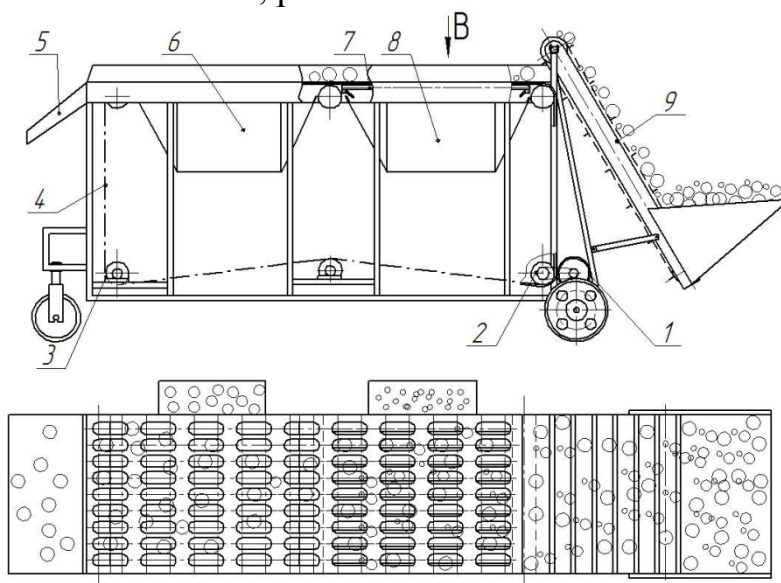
Схема запропонованої конструкції, з новим робочим органом транспортерного типу: 1 – приводний мотор-редуктор; 2 – ведучий барабан; 3 – підтримувальний барабан; 4 – транспортерна стрічка; 5 – лоток приймання великої фракції; 6 – лоток приймання середньої фракції; 7 – калібрувальне решето; 8 – лоток приймання дрібної фракції; 9 – транспортер для подачі з приймальним лотком.
